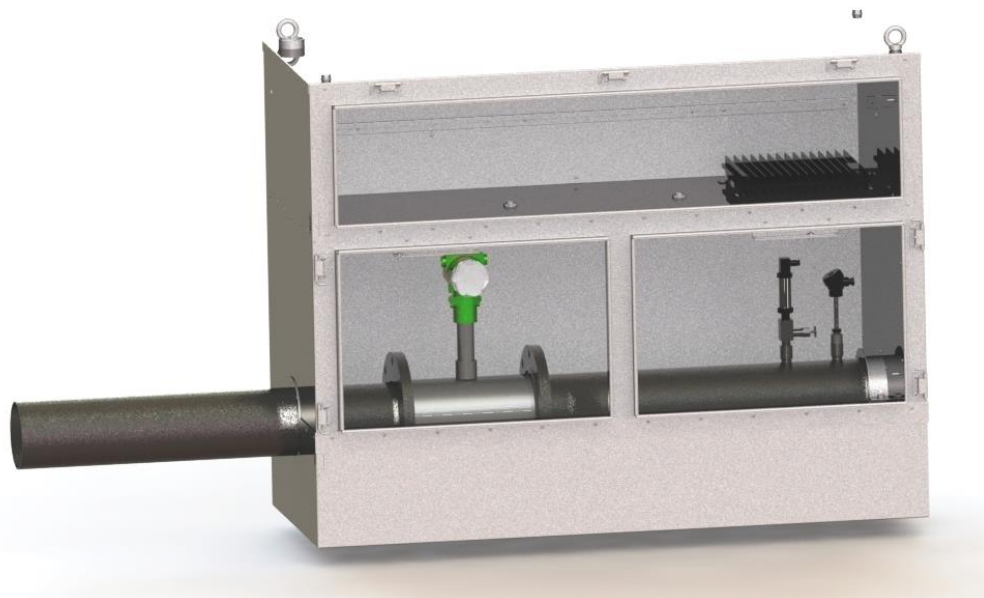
Шкаф трубный обогреваемый ШТО вертикального типа
